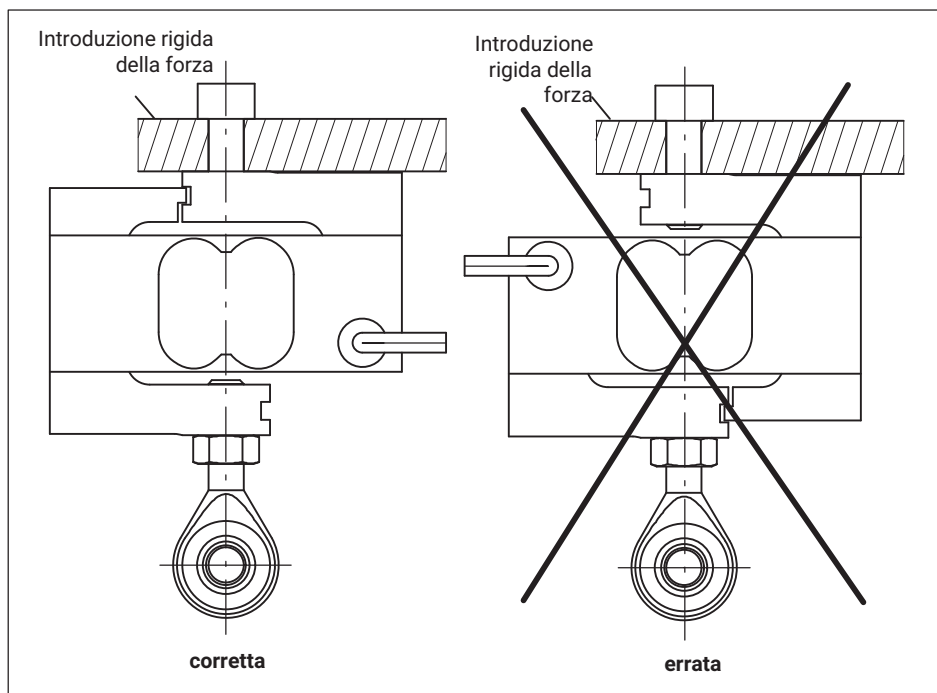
Orientamento del trasduttore durante il montaggio
